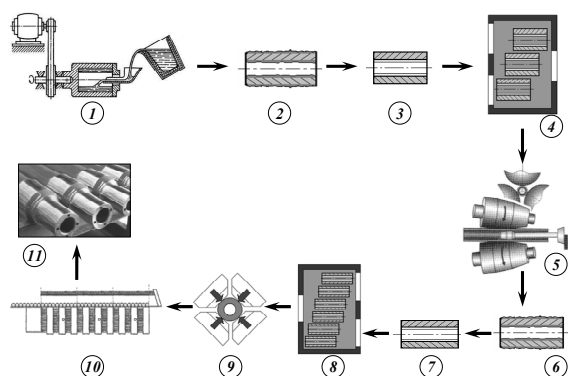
Вариант технологии изготовления оси из центробежнолитой заготовки (винтовая прокатка - ковка)
